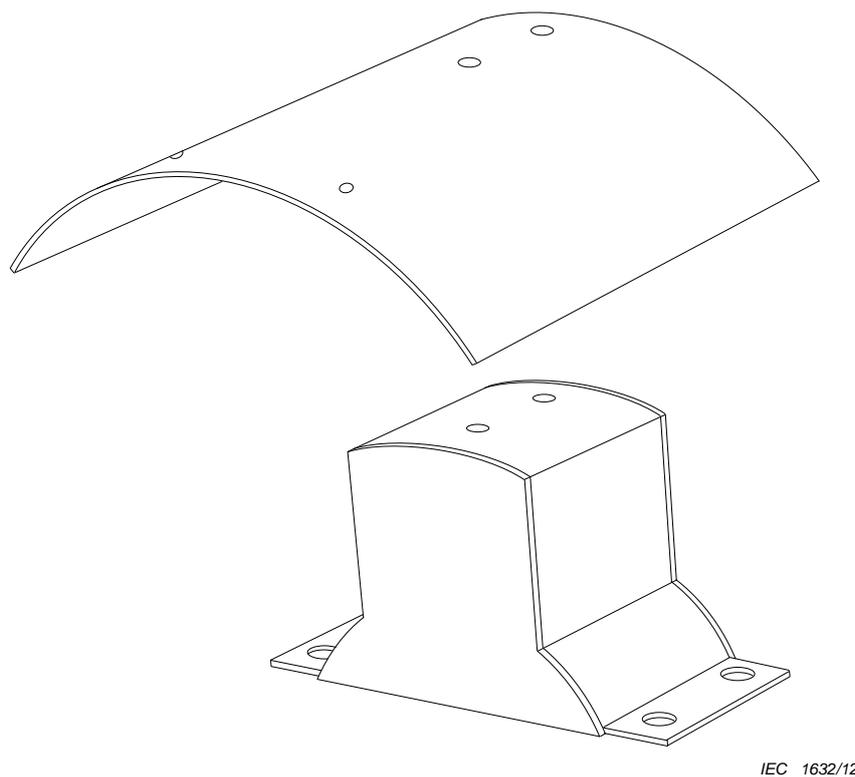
Montage d'essai pour bobine de champ à enroulement à fils jetés
